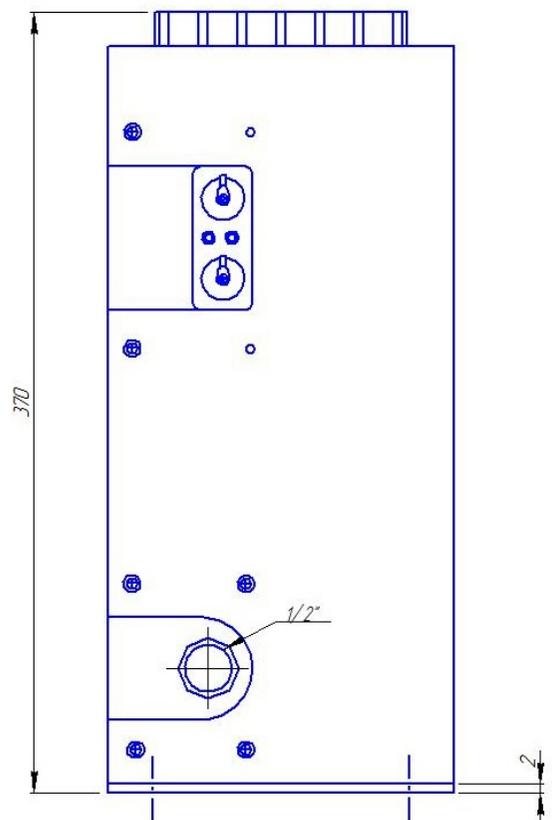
Габаритный чертёж TKMWS-10
